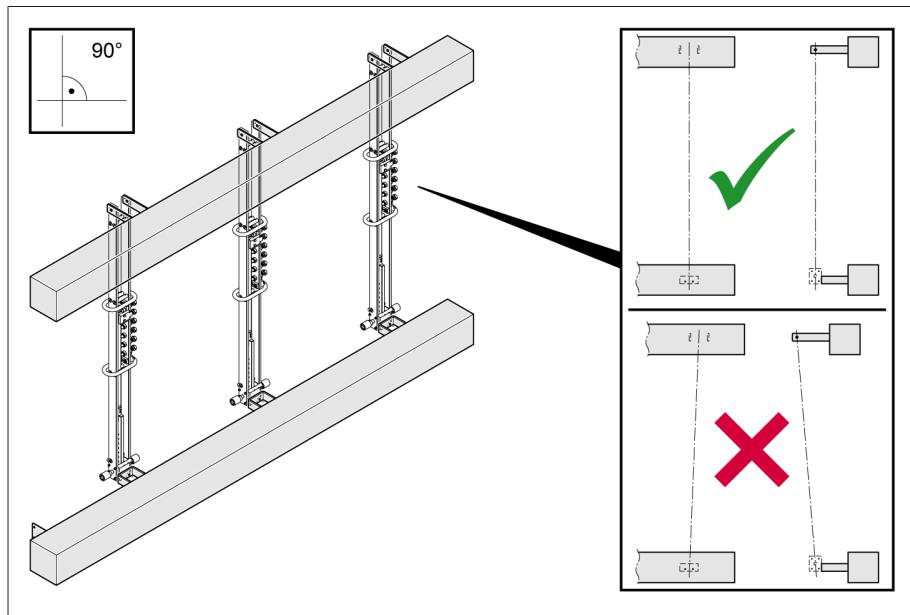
Крепежные приспособления, устройство ПБВ с боковым расположением контактов
